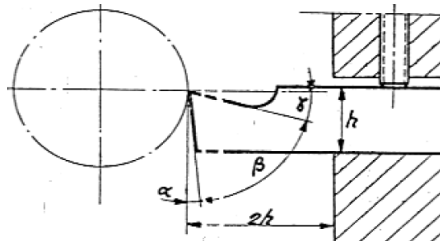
ângulos de corte Fonte - Carlos Sousa
